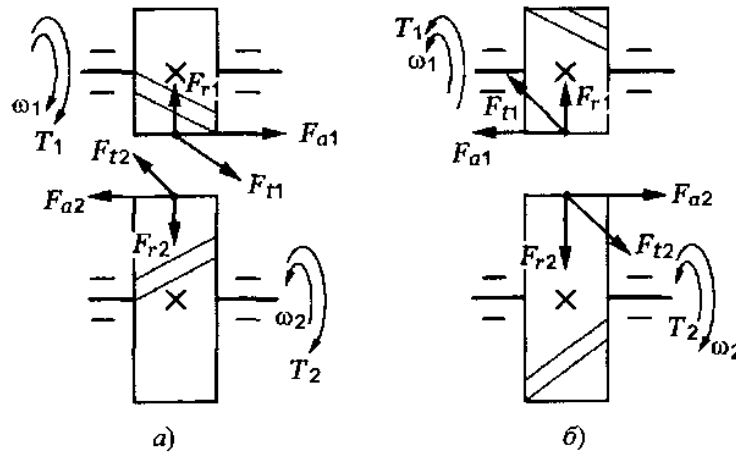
Схемы сил в зацеплении косозубой цилиндрической передачи: *а* — направление вращения быстроходного вала по часовой стрелке; *б* — направление вращения быстроходного вала против часовой стрелки
